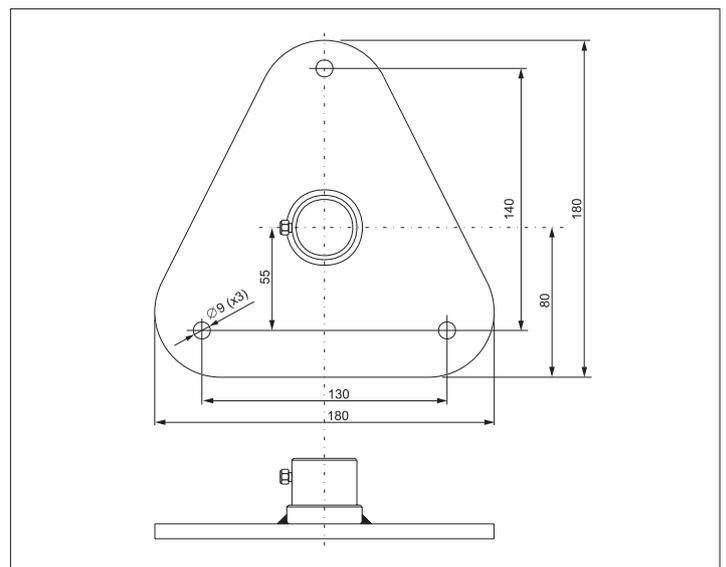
Base per fissaggio a pavimento (HD2013.78)
